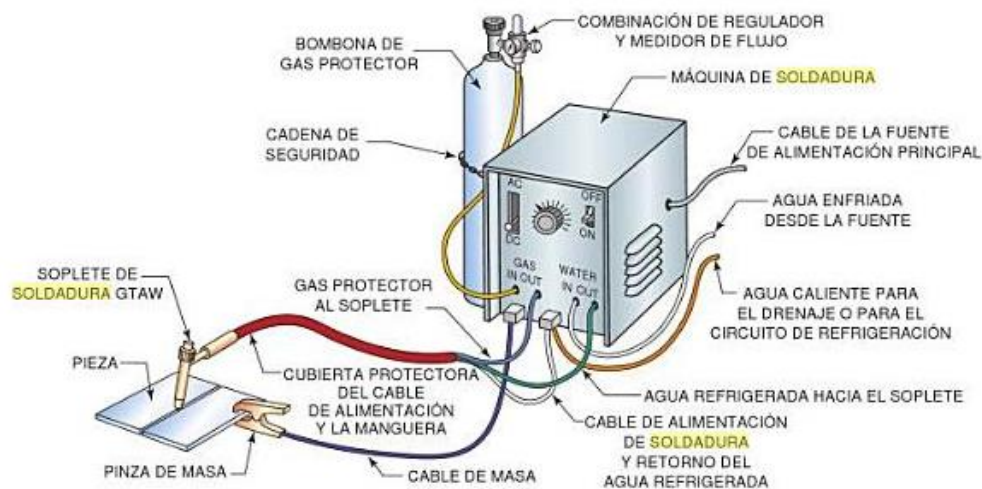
Soldadura GTAW. (Jeffus, 2009)
